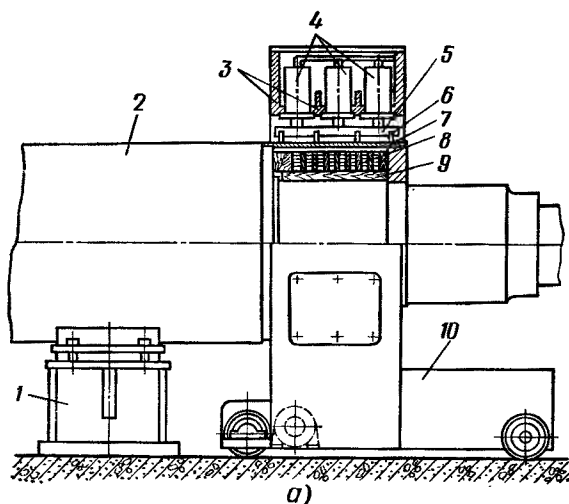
Прессовка лобовых частей обмотки ротора турбогенератора:
